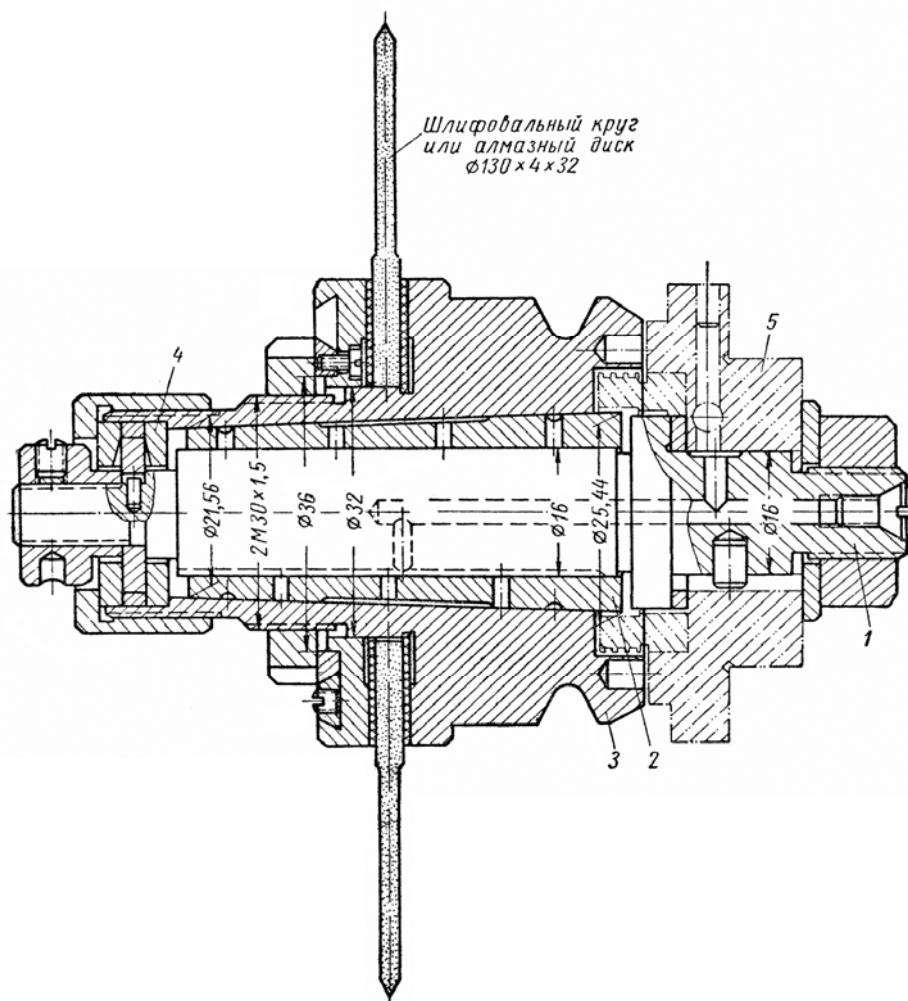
Шлифовальный шпиндель станка мод. Ш-228
